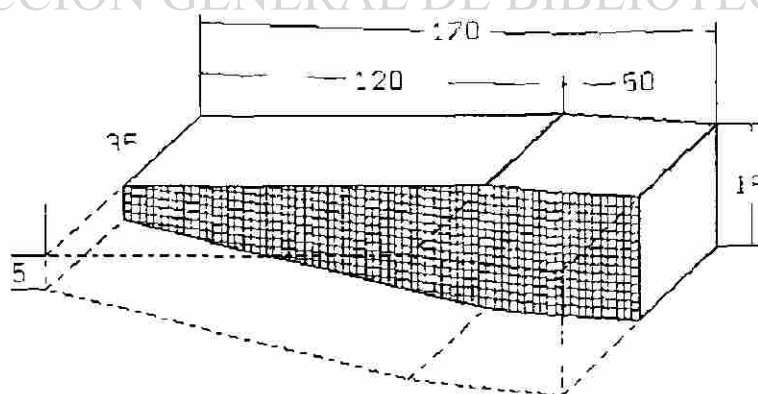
Probeta maquinada a partir del material a analizar.
